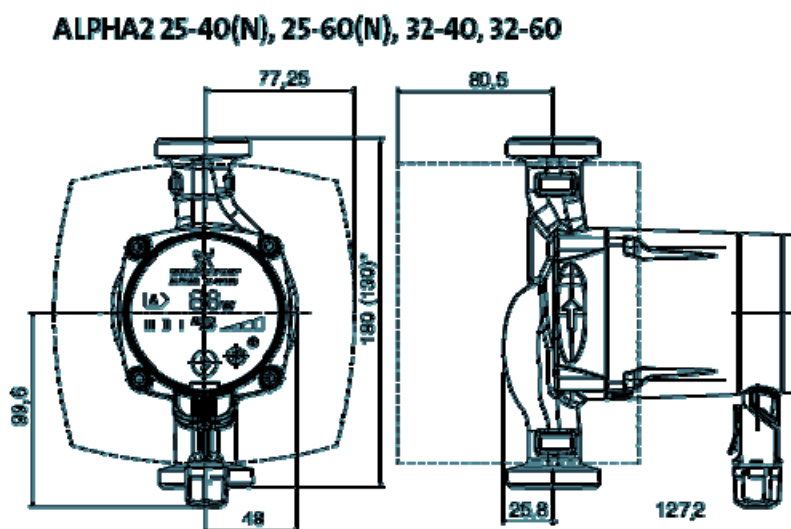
Pumpe: Abmessungen der Grundfos ALPHA 25-40 mit 180 mm Baulänge. Quelle: www.ecopumpen.de
